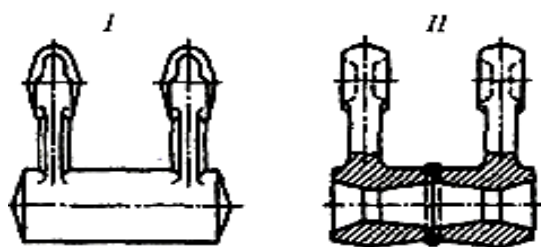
Упрощение способа штамповки путём последующей сварки отдельных частей заготовки
